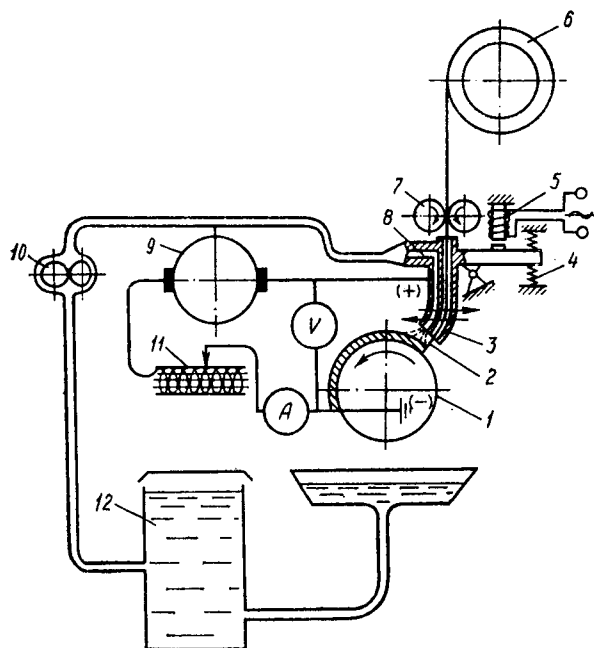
Схема установки для вибродуговой наплавки деталей:
